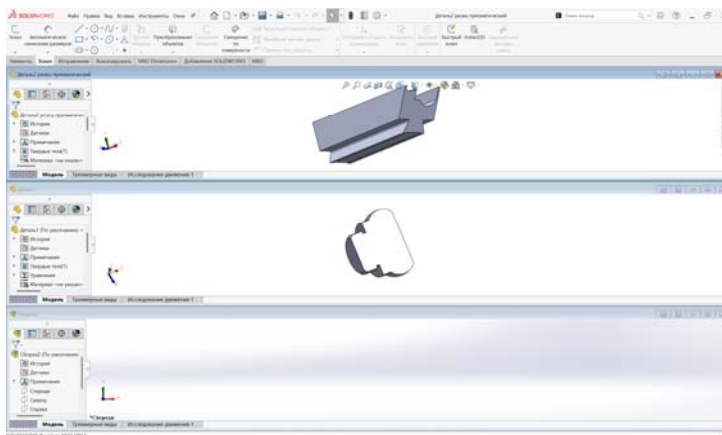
Перетаскивание твердотельной модели детали и твердотельной модели призматического фасонного резца в сборку
